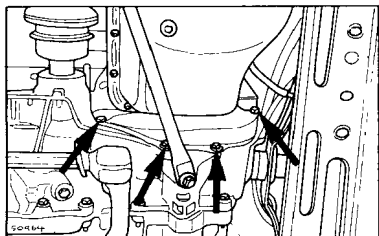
Крышка маховика между двигателем и коробкой передач
